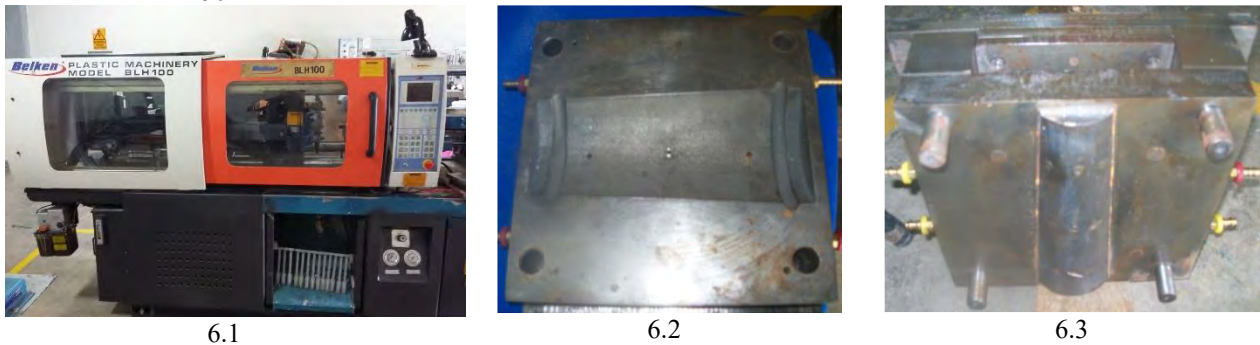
Partes principales de la máquina inyectora de Plástico. (6.1 Inyectora, 6.2 Molde parte fija, 6.3 Molde parte móvil).
